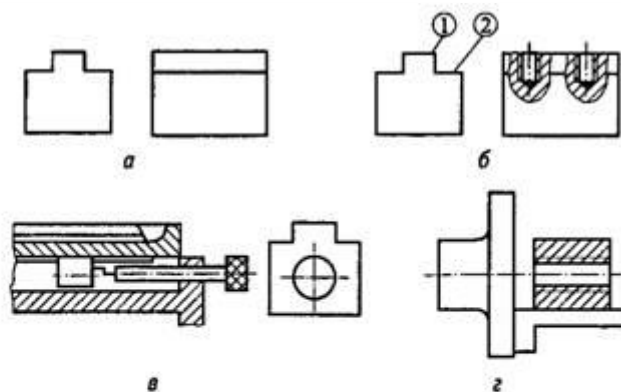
Последовательность изготовления нерегулируемой гайки хода винта:
